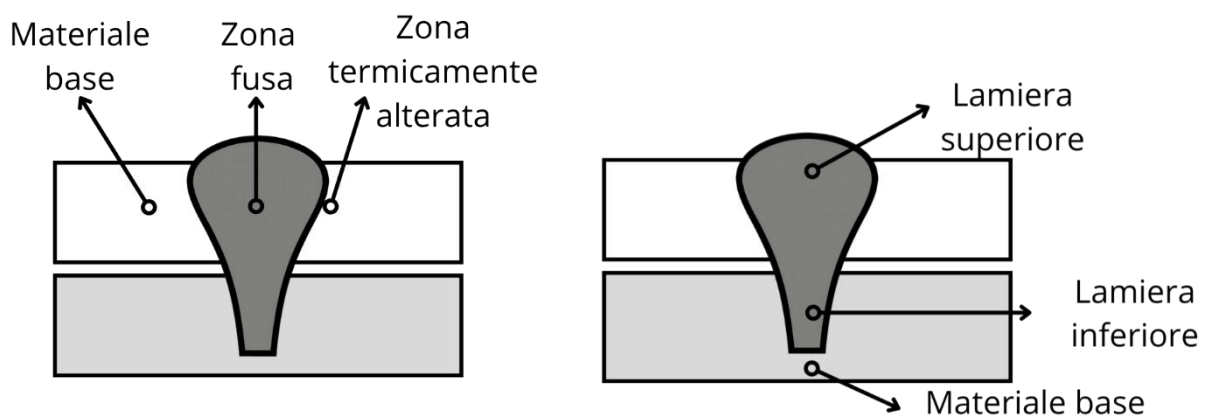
Schema esplicativo delle prove di durezza eseguite: a sinistra le misurazioni lungo la sezione trasversale del cordone, mentre a destra quelle lungo la sezione longitudinale
